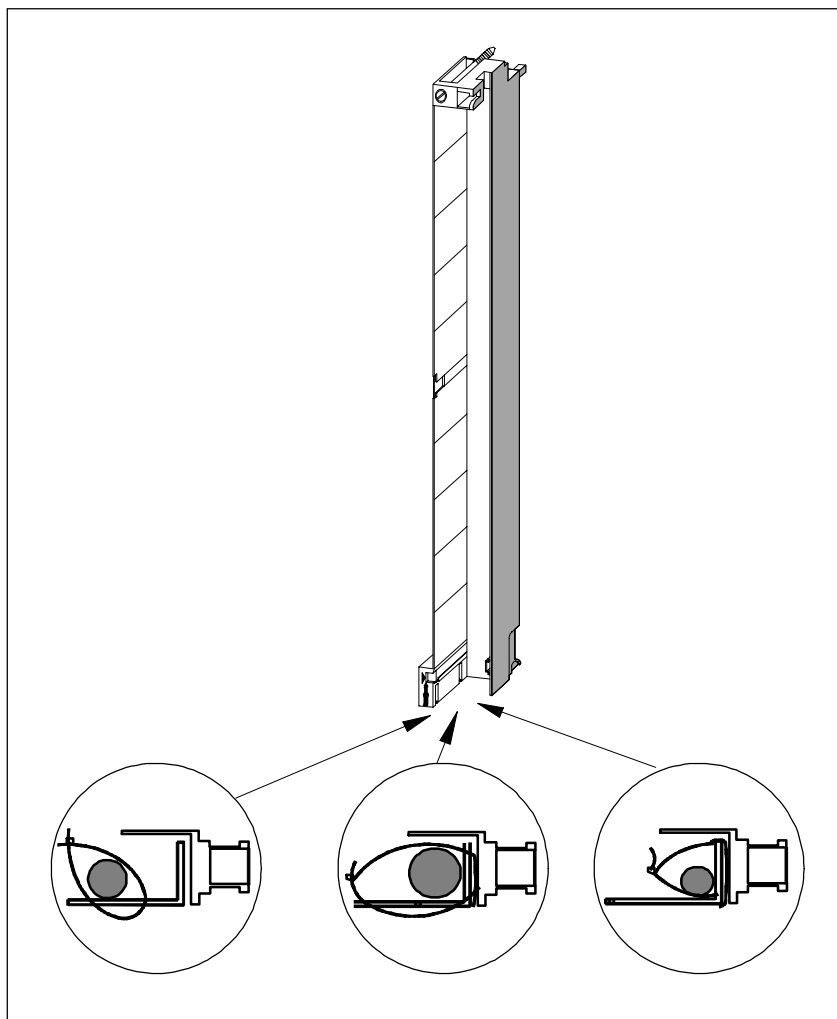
Закрепление кабеля для ослабления натяжения (вид снизу)
